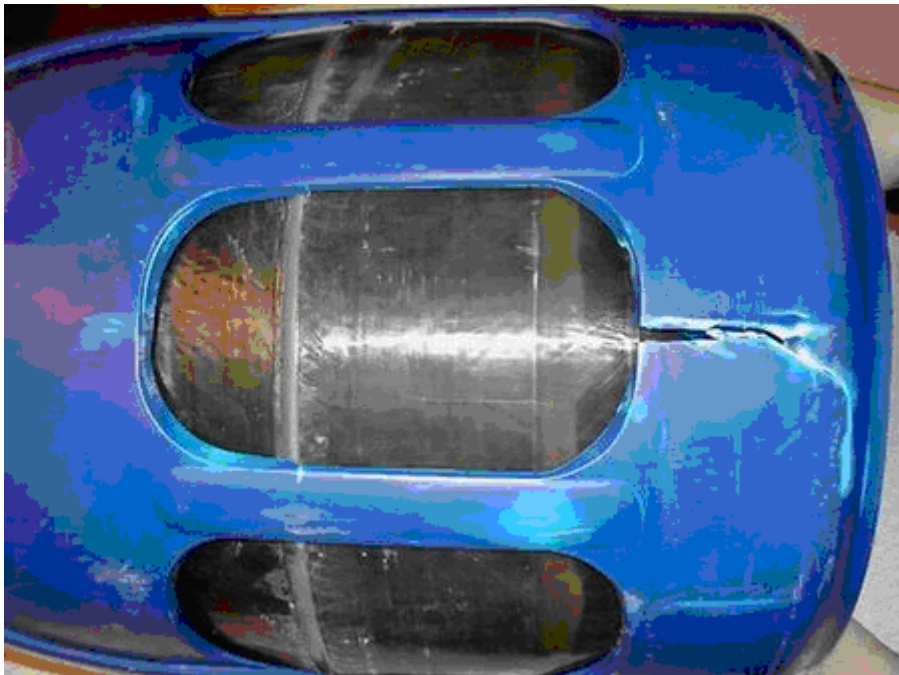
Fehlerhaftes Gehäuse: Gehäusebruch
